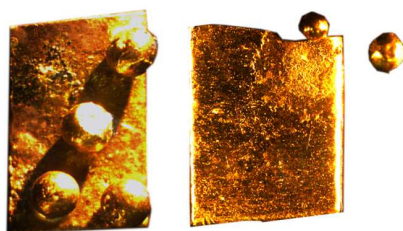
Soldadura mediante difusión de sal de Cu. Es visible la huella dejada por uno de los gránulos eliminado mecánicamente.
